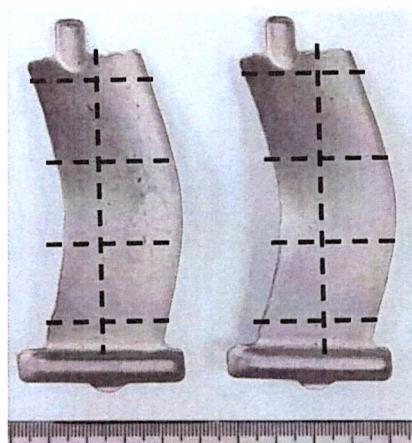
Гибридная аддитивная штамповка, с указанием схемы разрезки для изготовления микрошлифов
